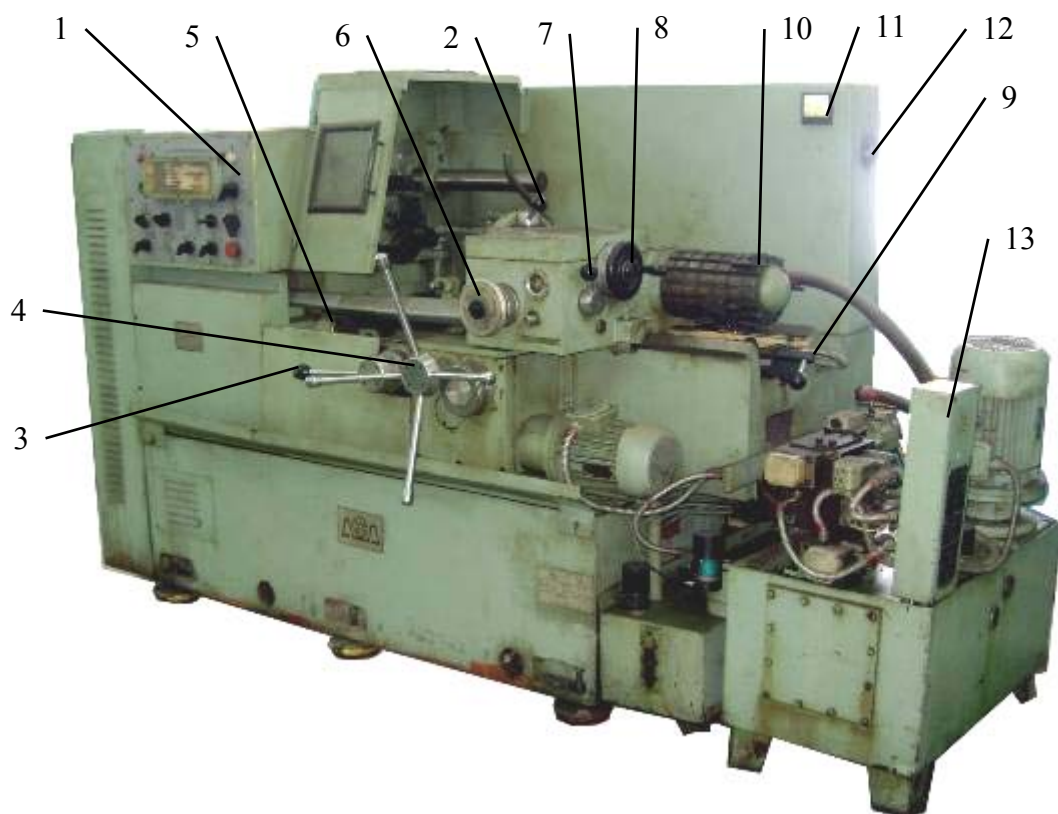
Общий вид и органы управления станка: 1 – панель управления; 2 – рукоятка фиксирования и расфиксирования револьверной головки; 3 – рукоятка включения и выключения механической продольной подачи револьверного суппорта; 4 – штурвал ручного продольного перемещения револьверного суппорта; 5 – рукоятка подвода упоров переднего барабана для отключения продольной подачи; 6 – маховик ручной поперечной подачи револьверной головки; 7 – рукоятка включения реверса поперечной подачи; 8 – маховик ручного быстрого поворота револьверной головки; 9 – рукоятка установки жесткого отводного упора для отключения продольной подачи; 11 – амперметр "Указатель загрузки главного двигателя"; 12 – вводной автомат; 13 – гидростанция
